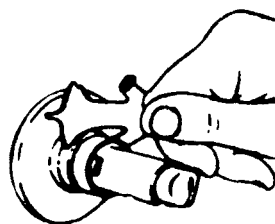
Крепление розочки с резьбой гаечным ключом (С разрешения компании Schlage Lock Company)
